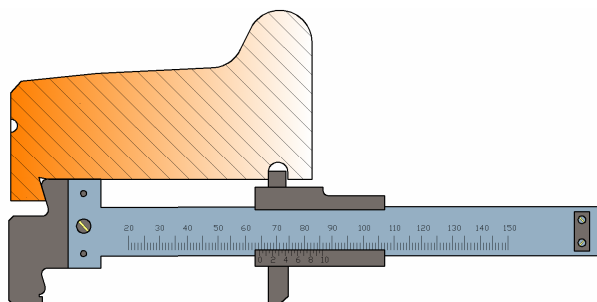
Posuvné měřidlo pro přenos šířky kotouč a obručí
